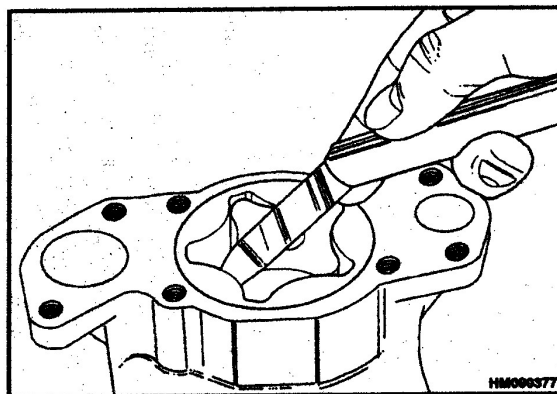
Проверка зазора внутреннего рабочего колеса.
